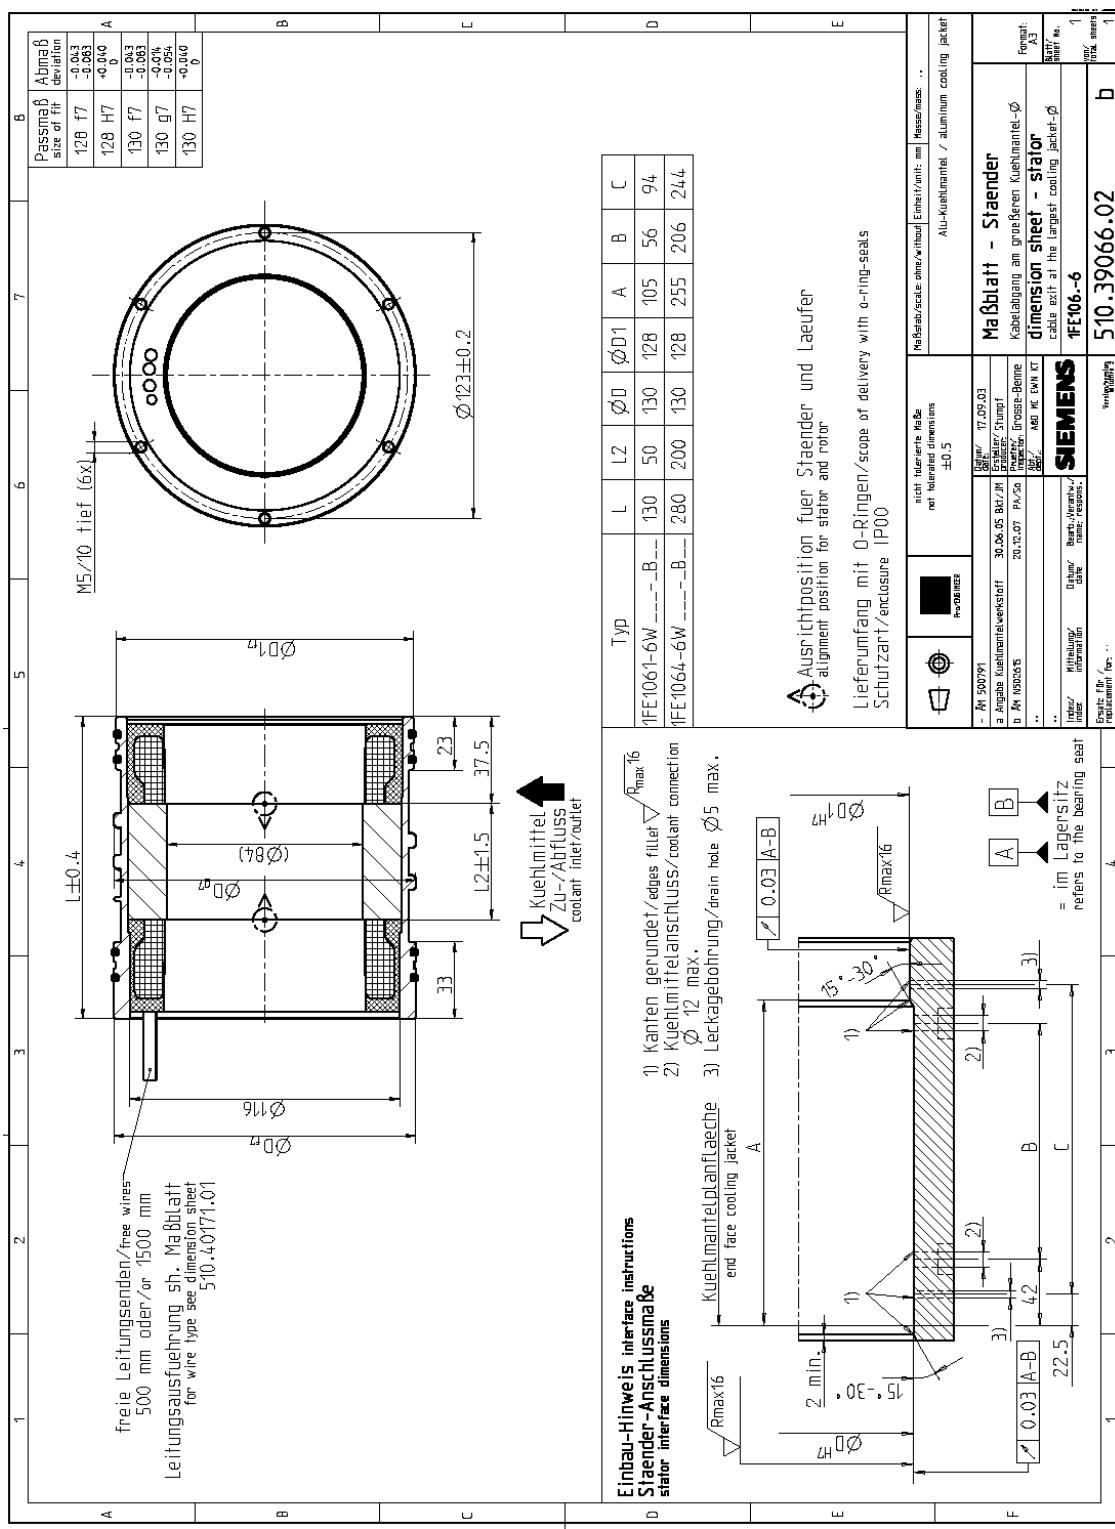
1FE106□-6, Ständer mit Kühlmantel, Kabelabgang am größeren Kühlmanteldurchmesser
